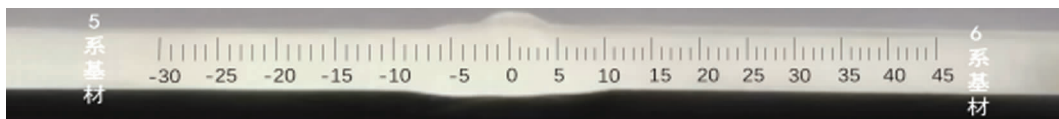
焊接接头硬度标线与测点位置(单位:mm)
